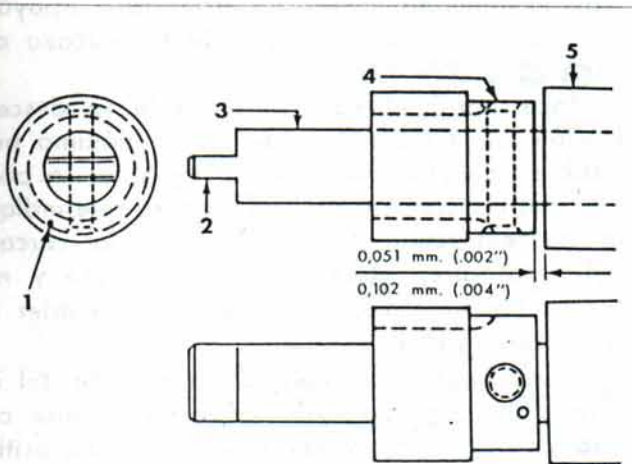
Detalle de la colocación del engranaje helicoidal de la bomba de aceite.
